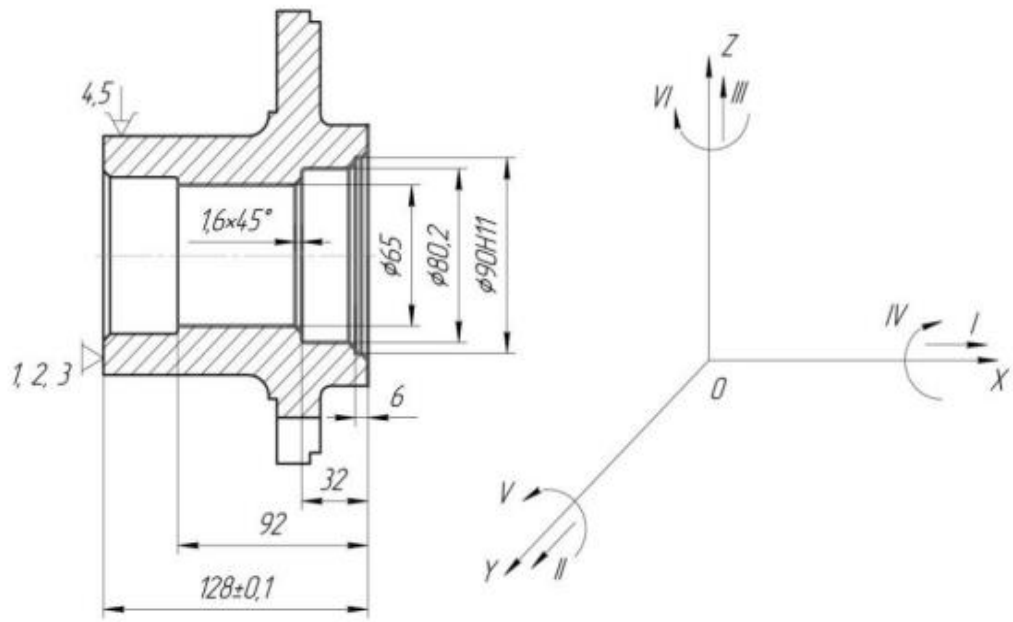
Схема базування заготовки в трьохкулачковому патроні на універсальному верстаті
